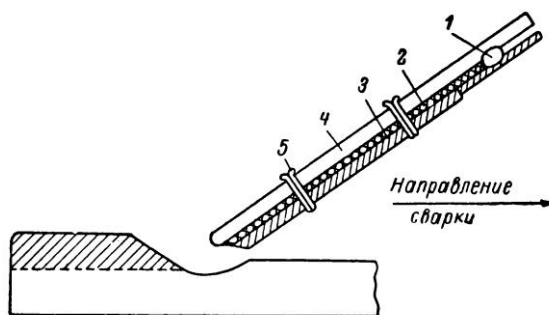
Схема сварки пучком электродов деталей:
